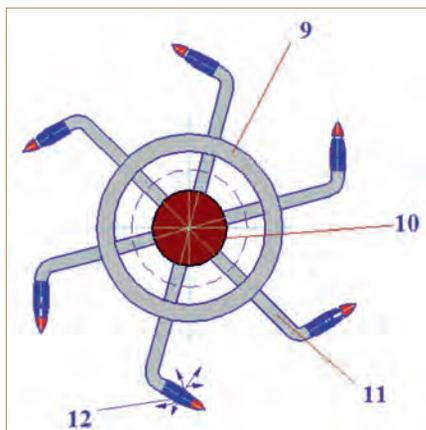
Рабочий орган почвообрабатывающего агрегата
